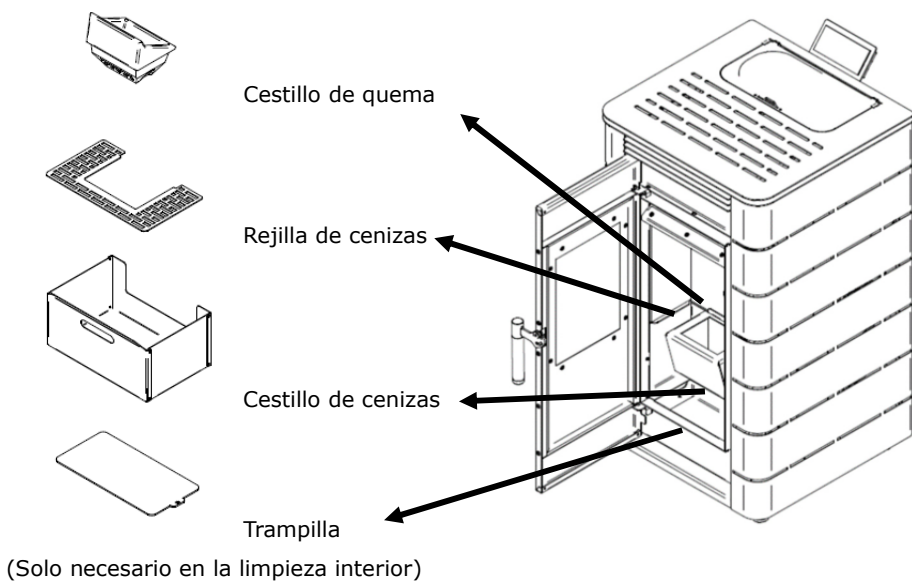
Accesorios a retirar en la limpieza del equipo E100 y E100R-UP
